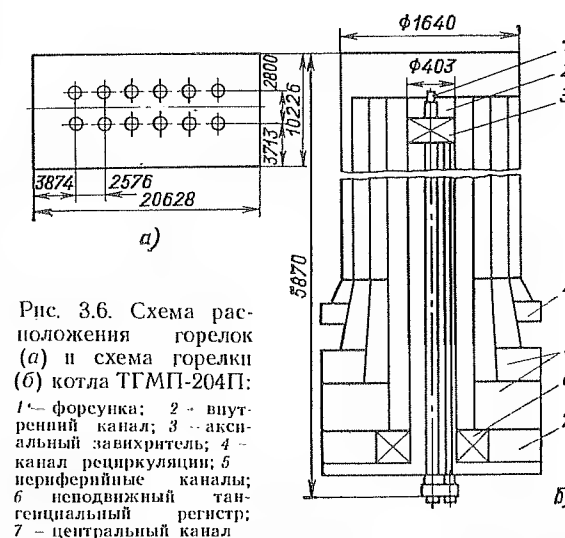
Схема расположения горелок (а) и схема горелки (б) котла ТГМП-204П: 1 — форсунка; 2 — внутренний канал; 3 — аксиальный завихритель; 4 — канал рециркуляции; 5 — периферийные каналы; 6 — неподвижный тангенциальный регистр; 7 — центральный канал
